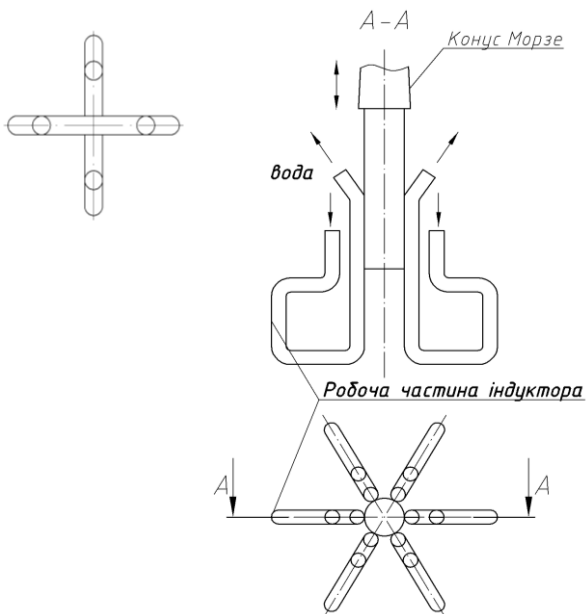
Індуктор для гартування півкруглих шлицевих поверхонь на шість позицій з окремими охолоджувальними камерами
